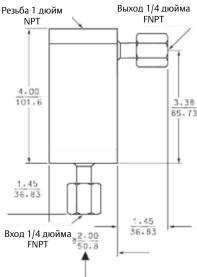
Габариты металлической проточной ячейки (S10240 и S10290)
